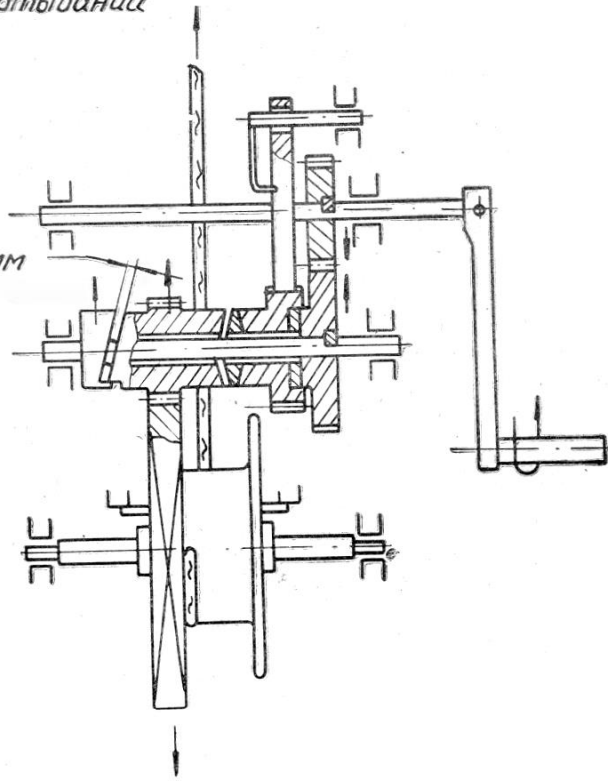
Схема механизма лебедки (стрелки показывают направление движения при свертывании мачты).
